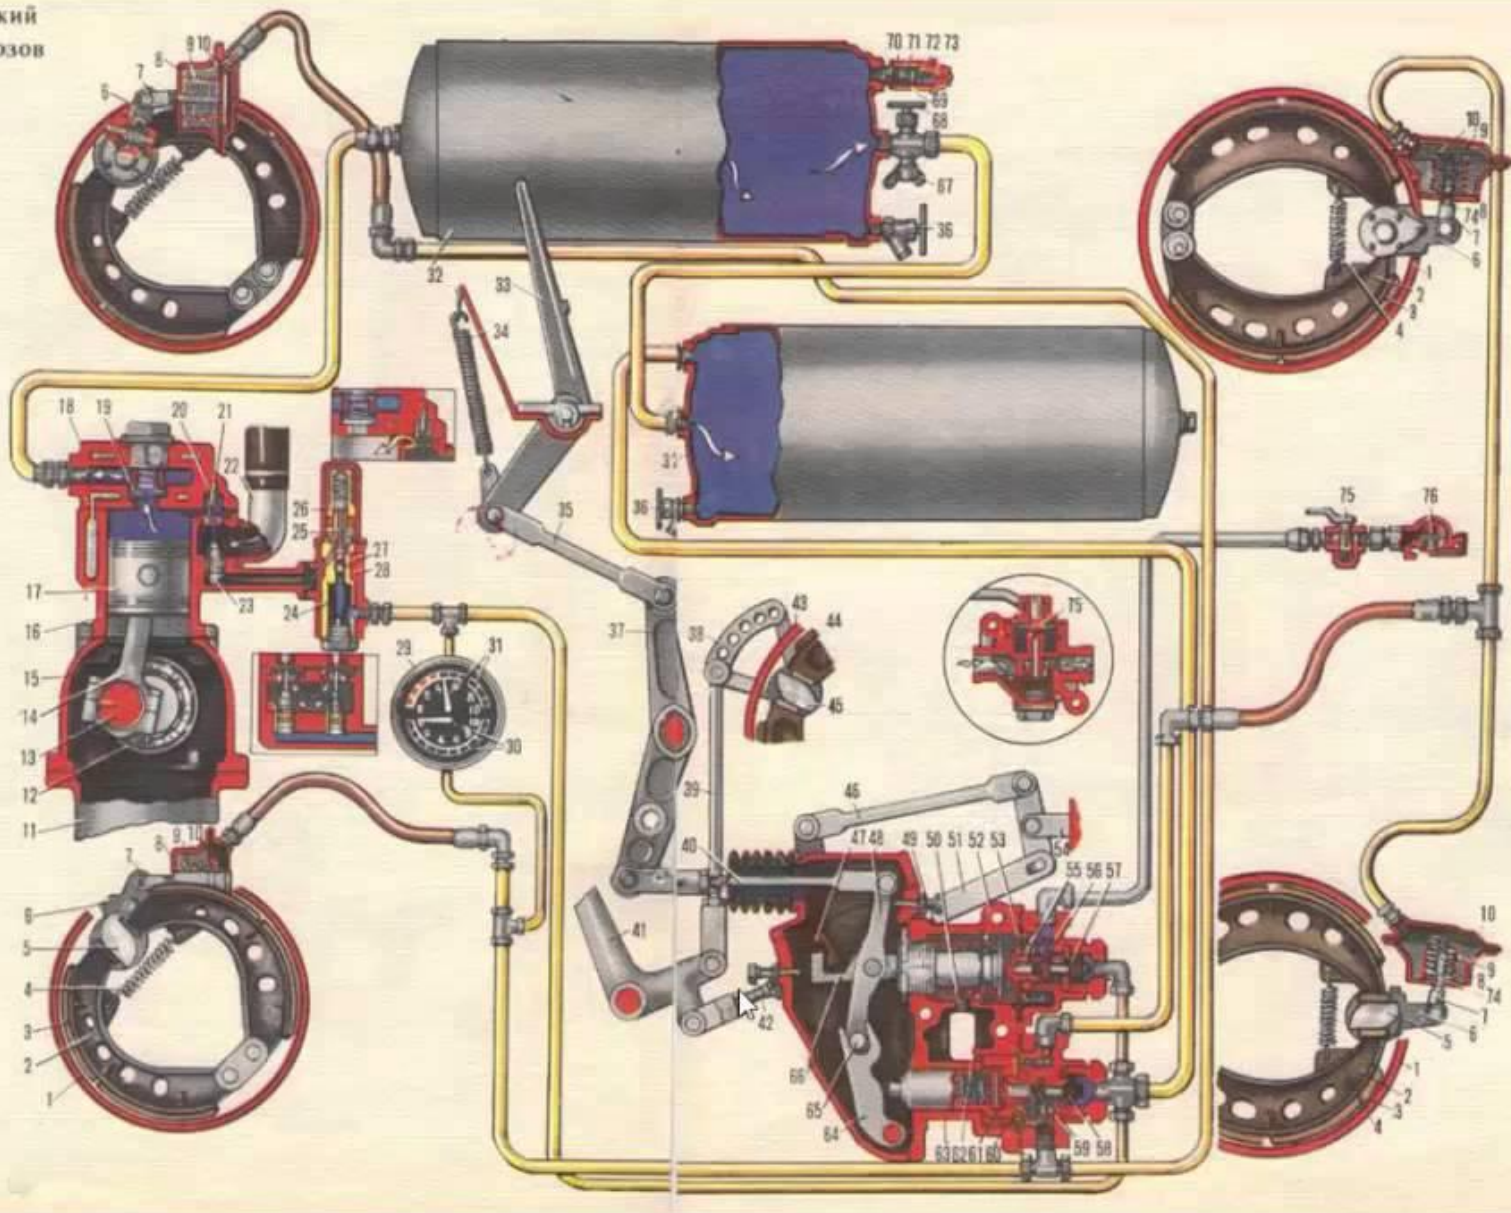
Схема пневматического привода гальм ЗІЛ-130
